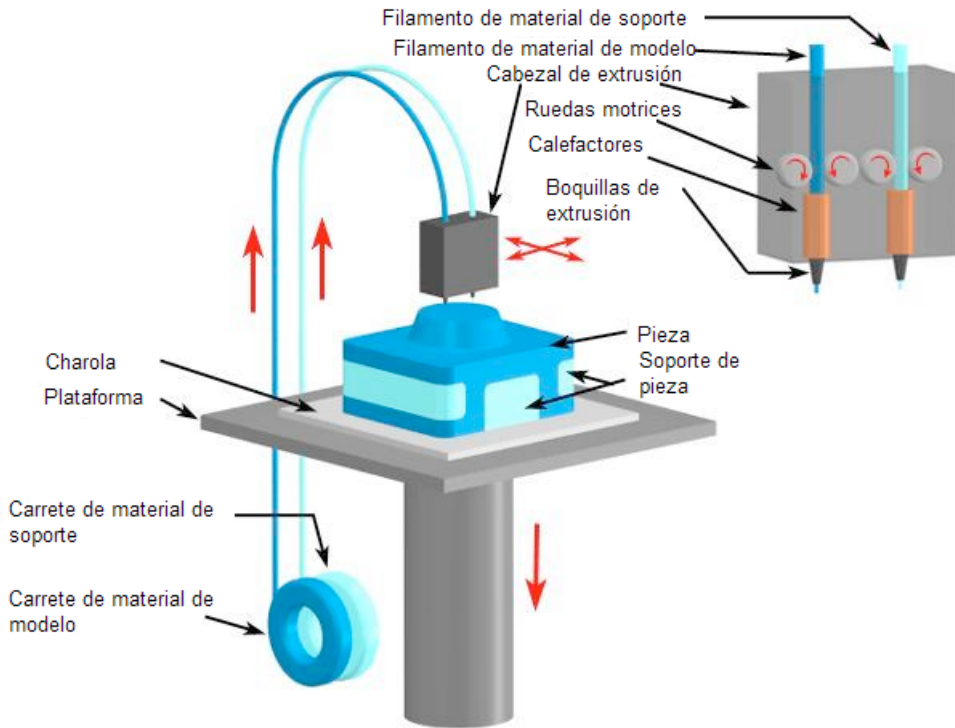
Proceso de Modelado por Deposición Fundida (FDM) [11]
